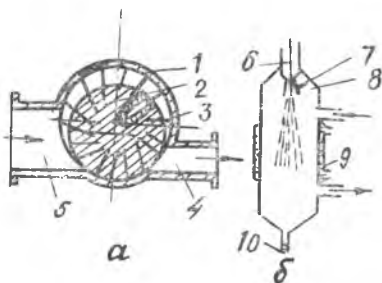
Схемы вакуумных насосов: а — многопластинчатого; б — пароструйного; 1 — корпус; 2 — ротор; 3 — пластины; 4 — выхлопной патрубок; 5 — всасывающий патрубок; 6 — пар; 7 — сопло; 8 — рабочая камера; 9 — охлаждение; 10 — сливной трубопровод
